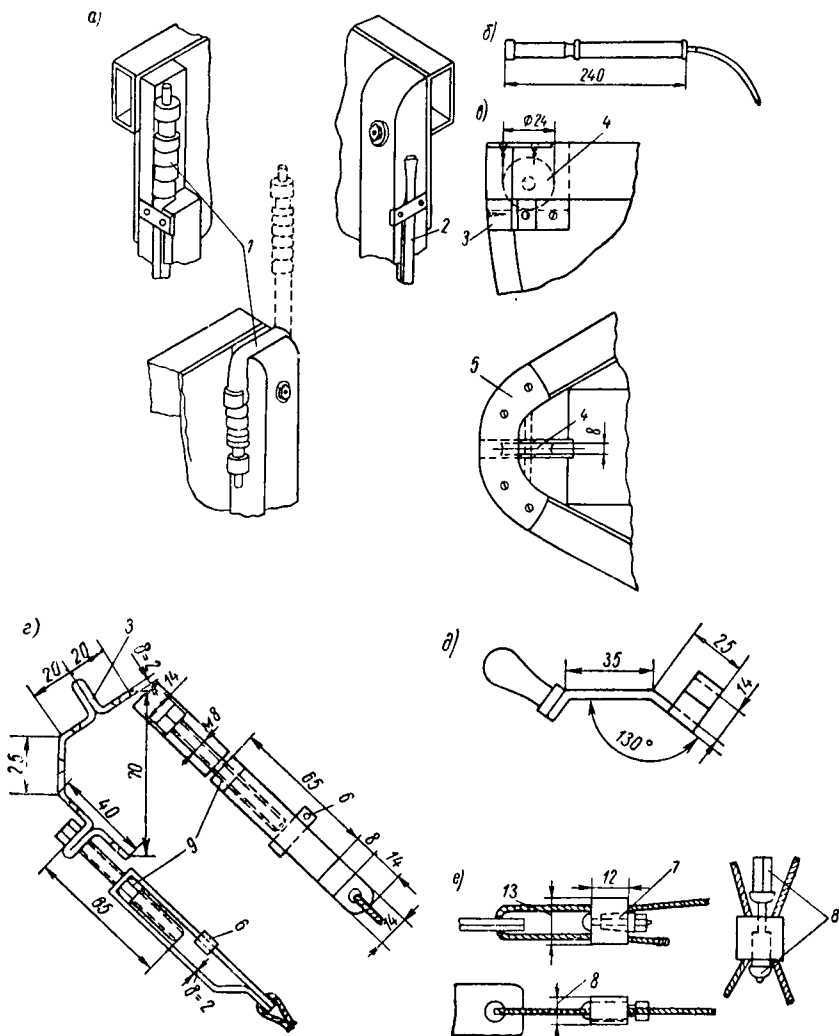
«Ладoga» М2-Б: а — пневматическое уплотнение на шпангоутах; б — насос (самого малого размера); в — шкив якорного канатика и основание натяжного приспособления на корме (вид сбоку и сверху); г — кормовое натяжное приспособление; д — торцевой ключ; е — зажимы для закрепления и регулировки натяжения троса (две конструкции).
